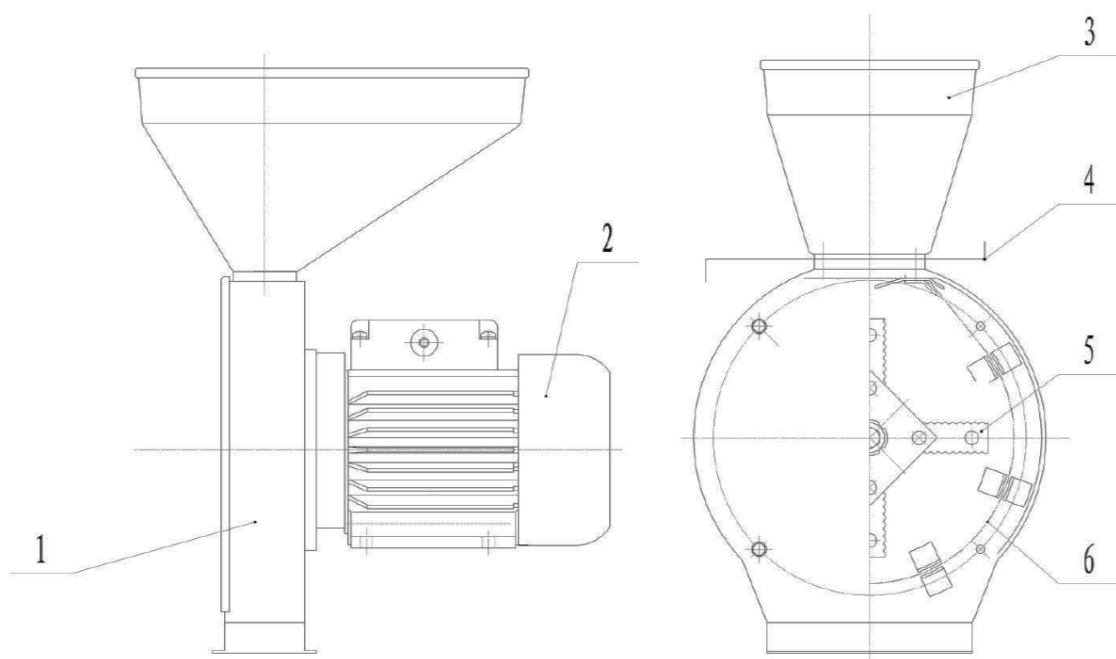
Устройство кормоизмельчителя КБЭ-180 «Дон»: 1 – корпус кормоизмельчителя; 2 – двигатель; 3 – загрузочная воронка для зерна; 4 – регулировочная заслонка для подачи зерна; 5 – ротор; 6 – сито
